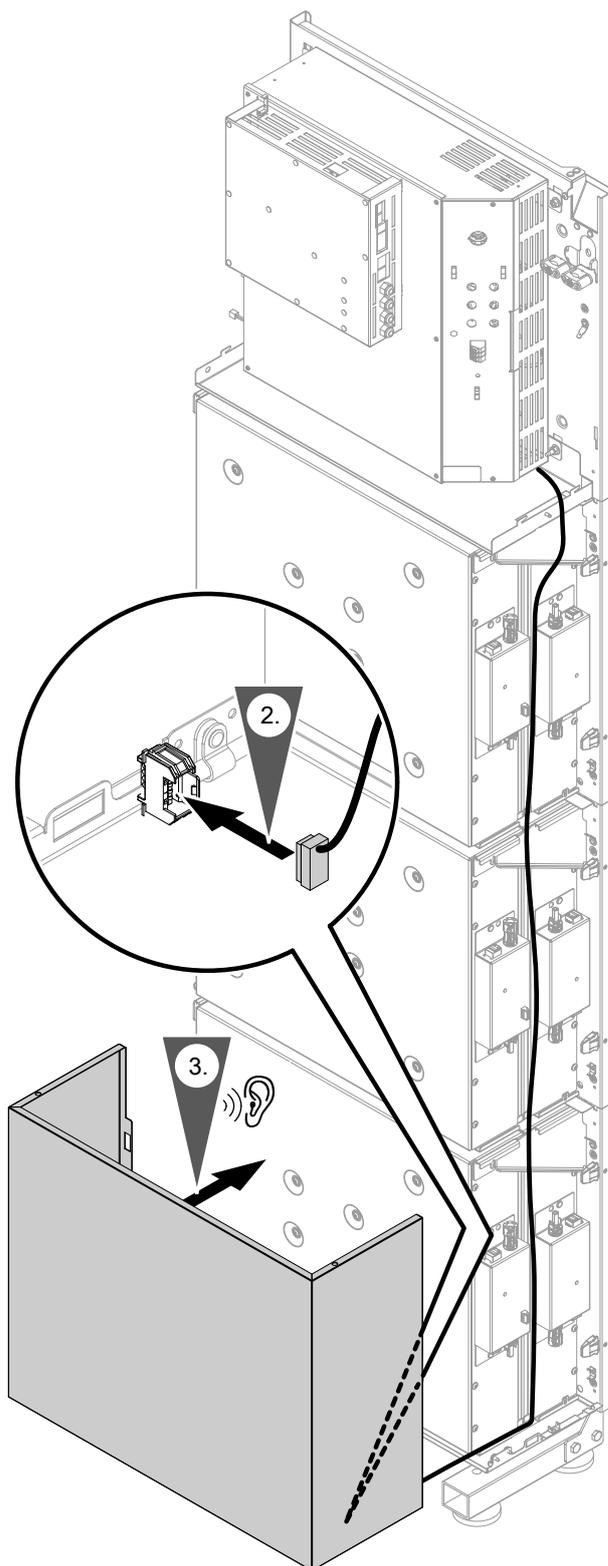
Esempio: kit montaggio a pavimento L con Vitocharge VX3, tipo 4.6A12
